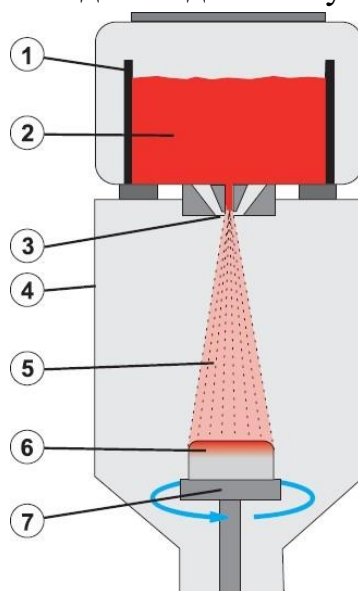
Схема отримання заготовок для виробництва заливних алюмінієвих гільз за технологією Silitec: 1 – ливарний тигель, 2 – розплав, 3 – кільцеве сопло, 4 – камера розпилення, 5 – конус розпилення, 6 – заготовка, 7 – обертова тарілка [21]
